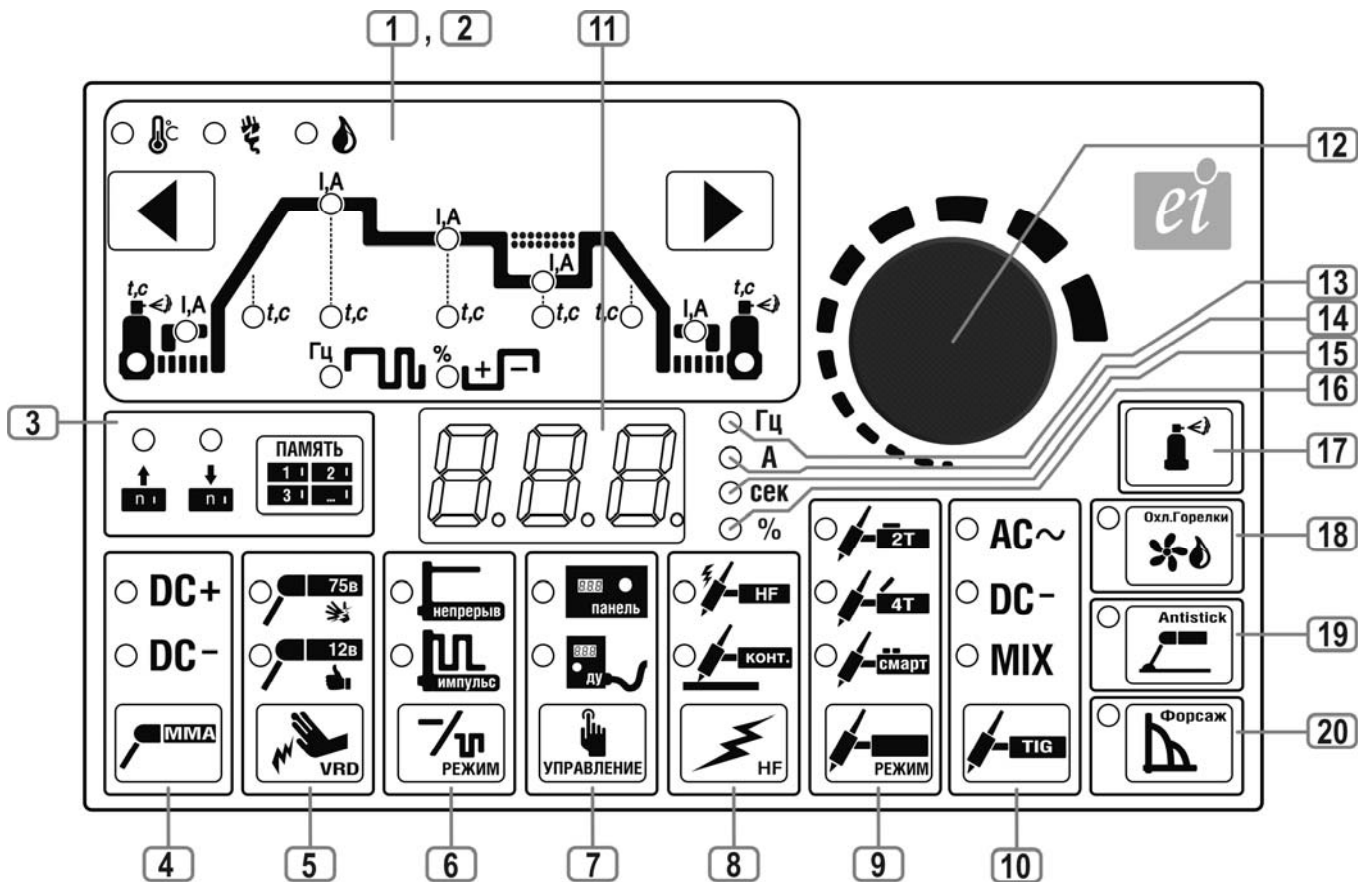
ВНЕШНИЙ ВИД ВЫПРЯМИТЕЛЯ ДЛЯ АРГОДУГОВОЙ СВАРКИ NEON ВД 201 АД
